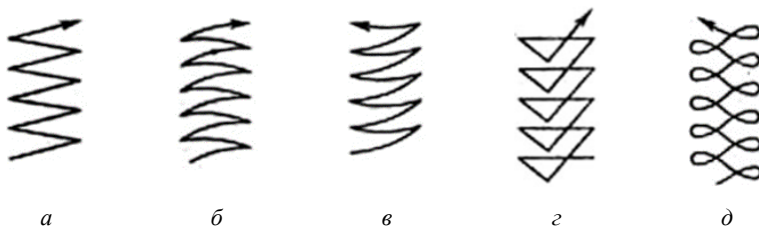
Виды колебательного движения электрода при ручной сварке
